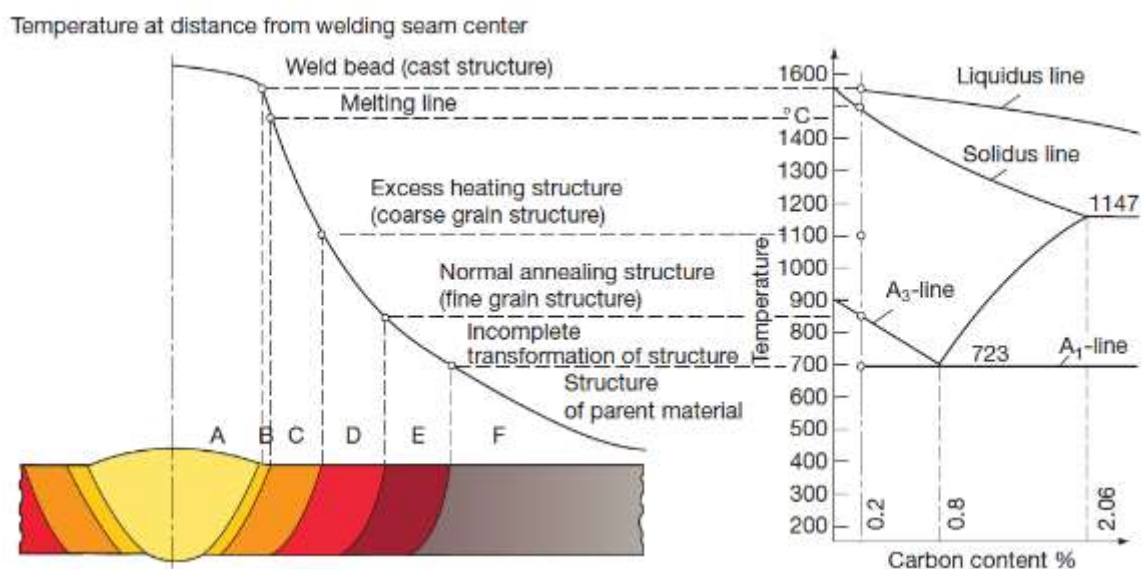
1 Variación de la estructura de la soldadura con la distancia desde el centro del cordón de soldadura [3]
